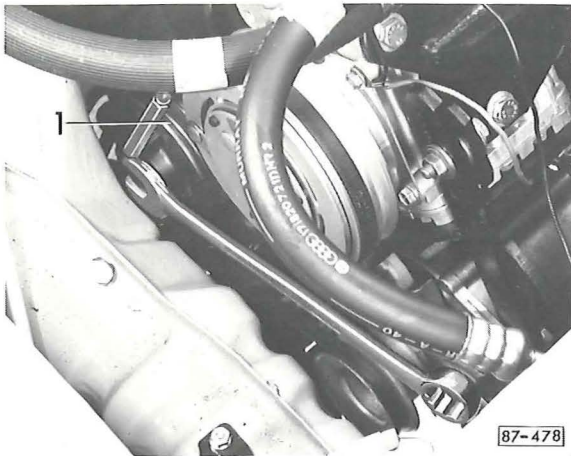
Réglage de la courroie trapézoïdale du compresseur
